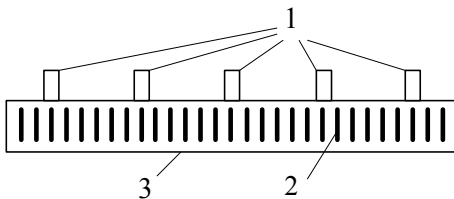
Пластинчатый сонотрод для ультразвуковой сварки пластмасс; 1 – стержни для подключения генераторов; 2 – прорези; 3 – рабочая поверхность.
